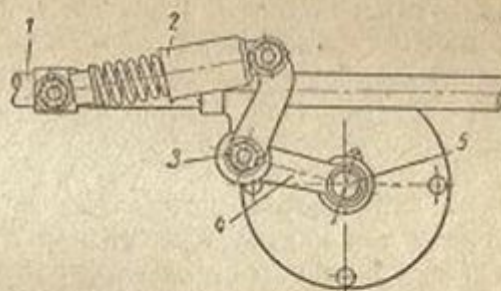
Рычажная подвеска колеса коляски мотороллера Т-200:
